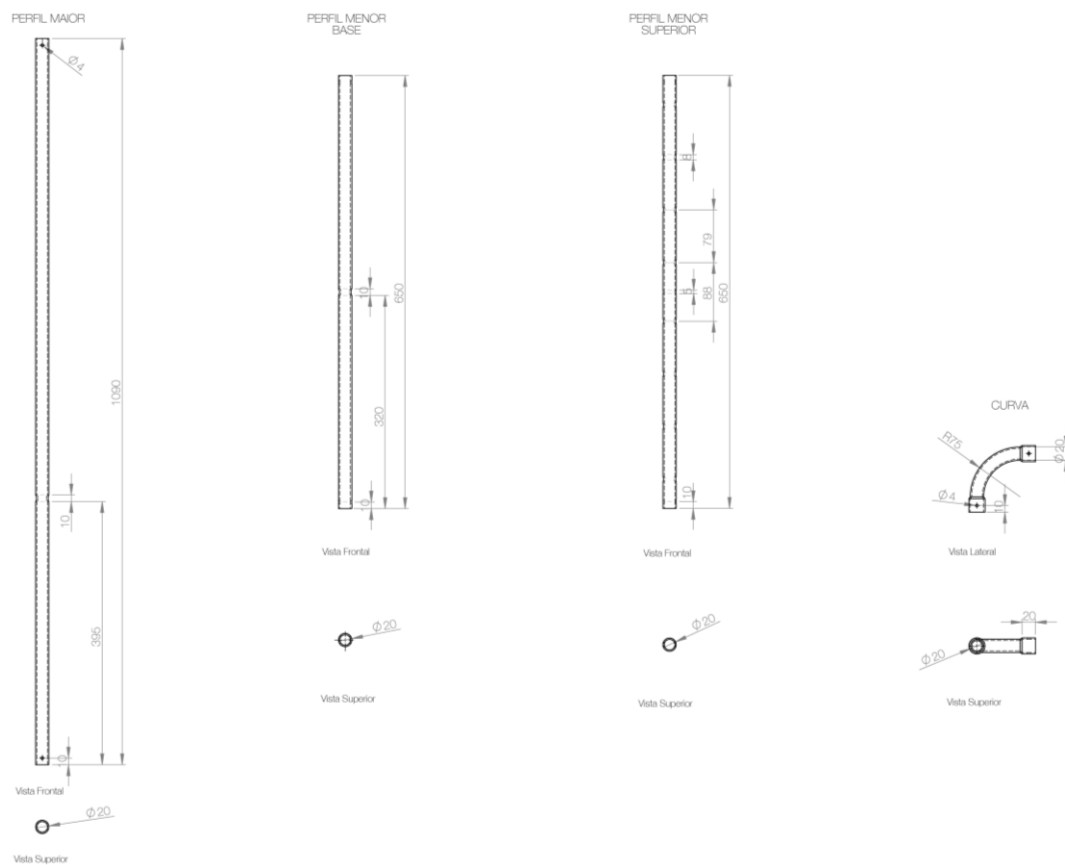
Desenho técnico das peças que compõem o aro da estrutura.
